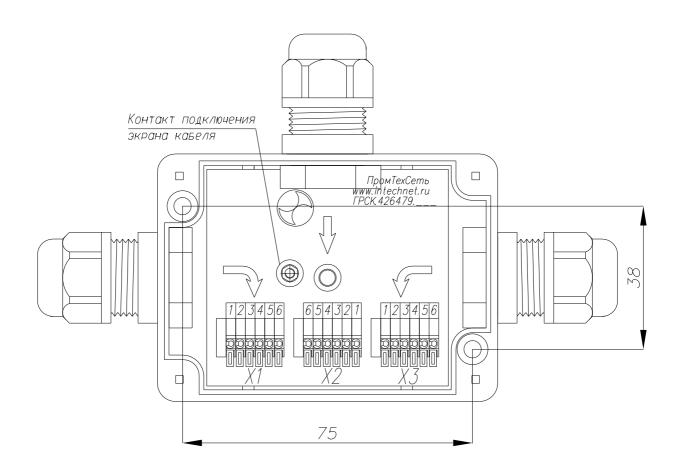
Компоновка и разметка места установки разветвителя
